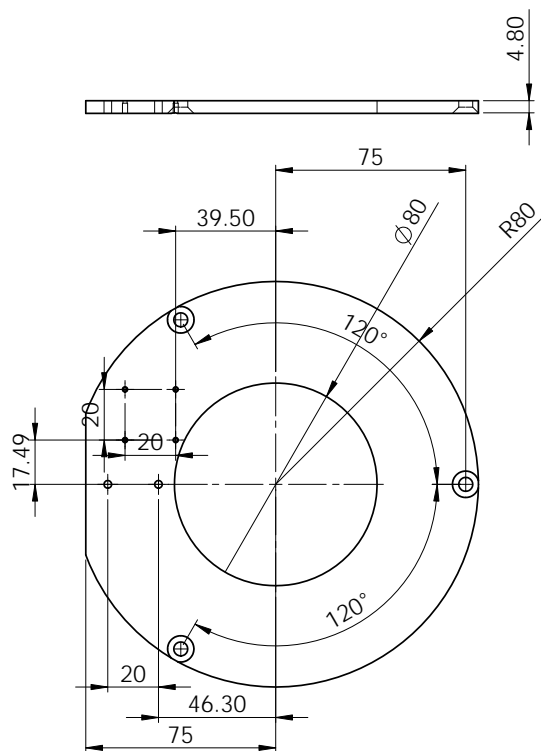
Technische Zeichnung des Ringaufsatzes.
